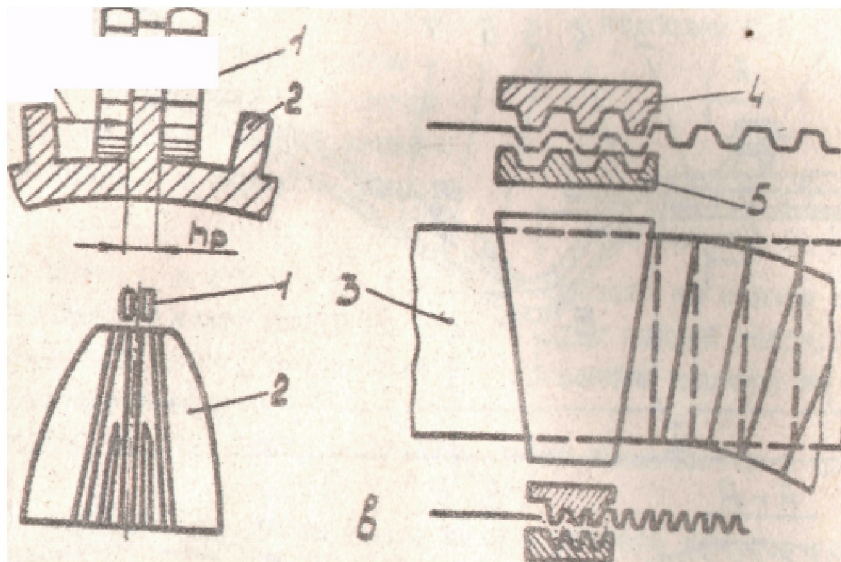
Схемы фрезерования канавок на наружной поверхности стенки (а), удвоения ребер (б) и штамповки гофров (в):
